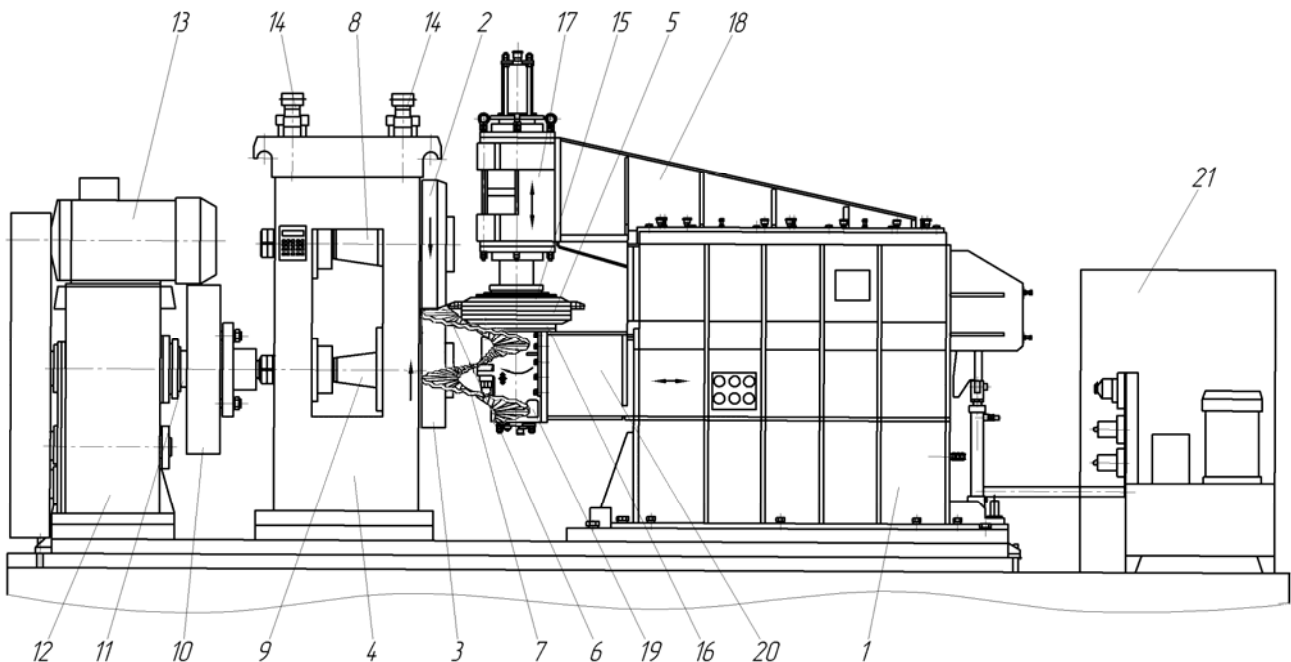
Схема установки для виготовлення ГГЗ методом прокатування
